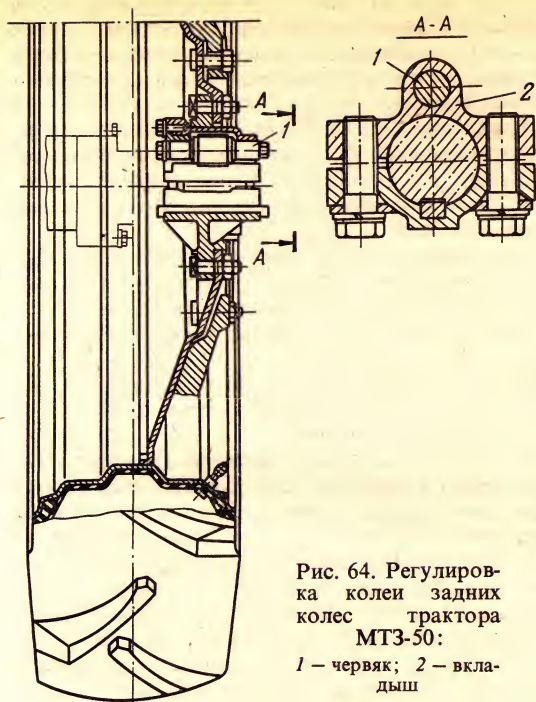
Регулировка колес задних колес трактора МТЗ-50:
